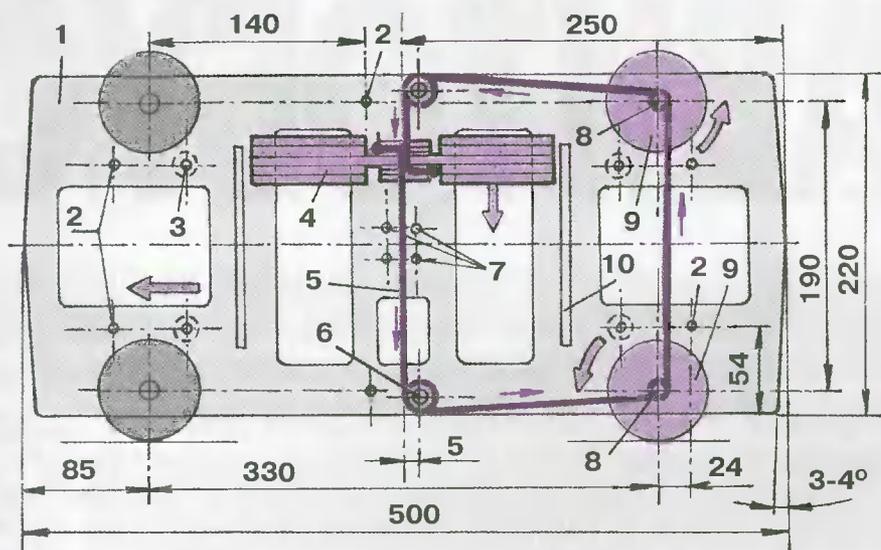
Размеры рамы модели и кинематическая схема: 1 — боковины рамы (2 шт.); 2 — отверстия для рычагов шторок днища; 3 — крепежные отверстия для резьбовых шпилек; 4 — груз; 5 — рабочая нить; 6 — направляющий шкив; 7 — крепежные отверстия ручки; 8 — ведущие валы (2 шт., диаметр 6 мм); 9 — ведущие колеса модели; 10 — паз для установки проставок.
